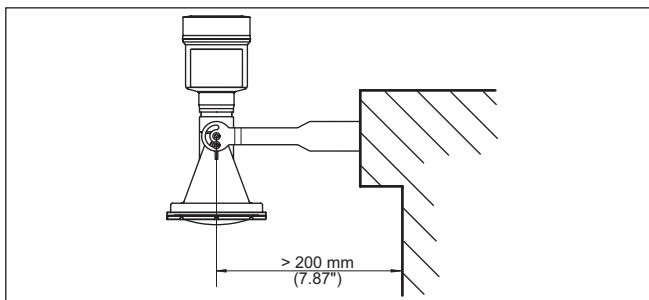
Montagem horizontal na parede com suporte de montagem de 170 mm de comprimento
